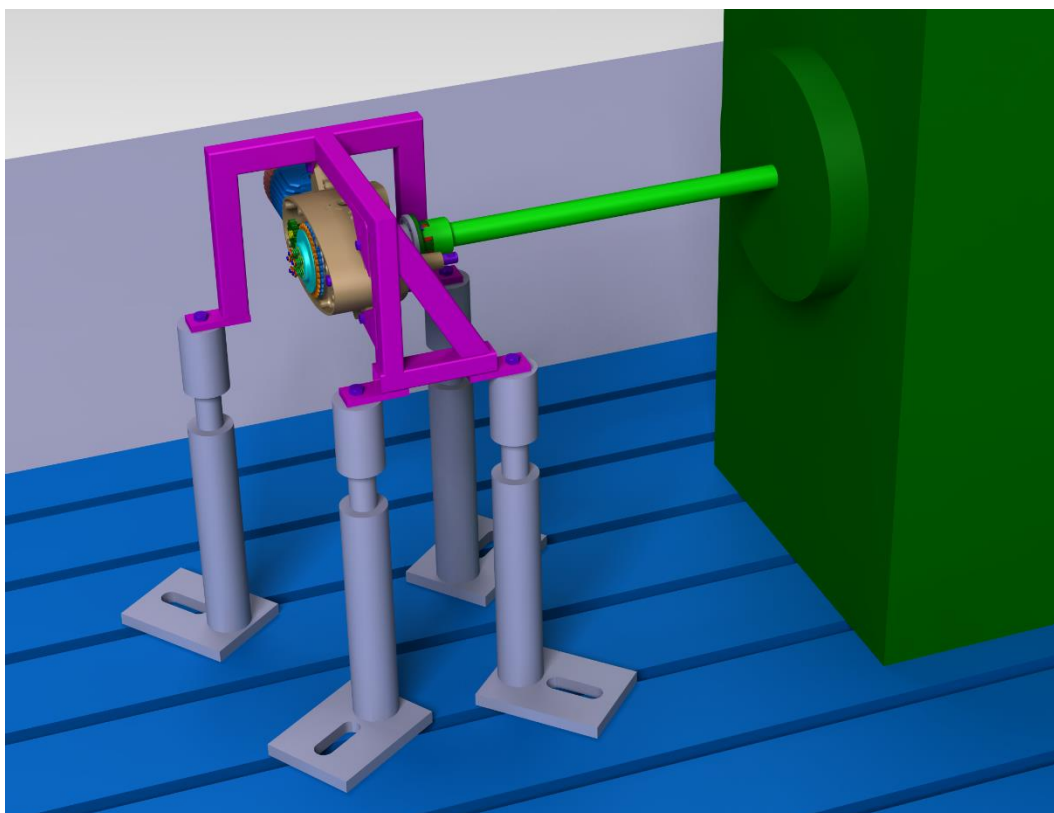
Varianta připojení motoru soustavou řetězových převodů
